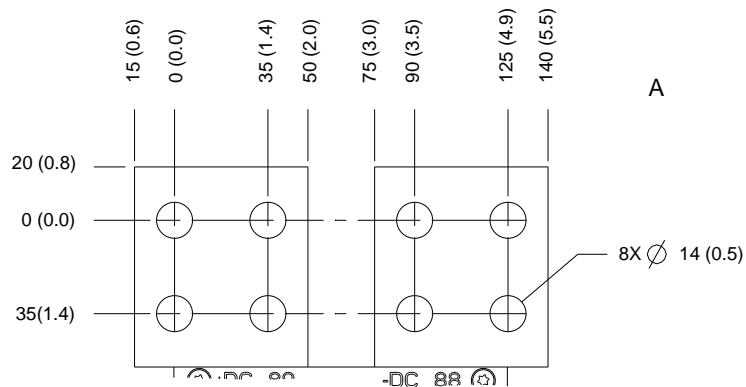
Dimensions des bornes de répartition de la charge/régén. E3h (vues latérales)
